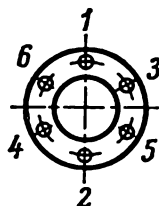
Ordre de serrage des écrous d'un flasque ou d'un couvercle rond
